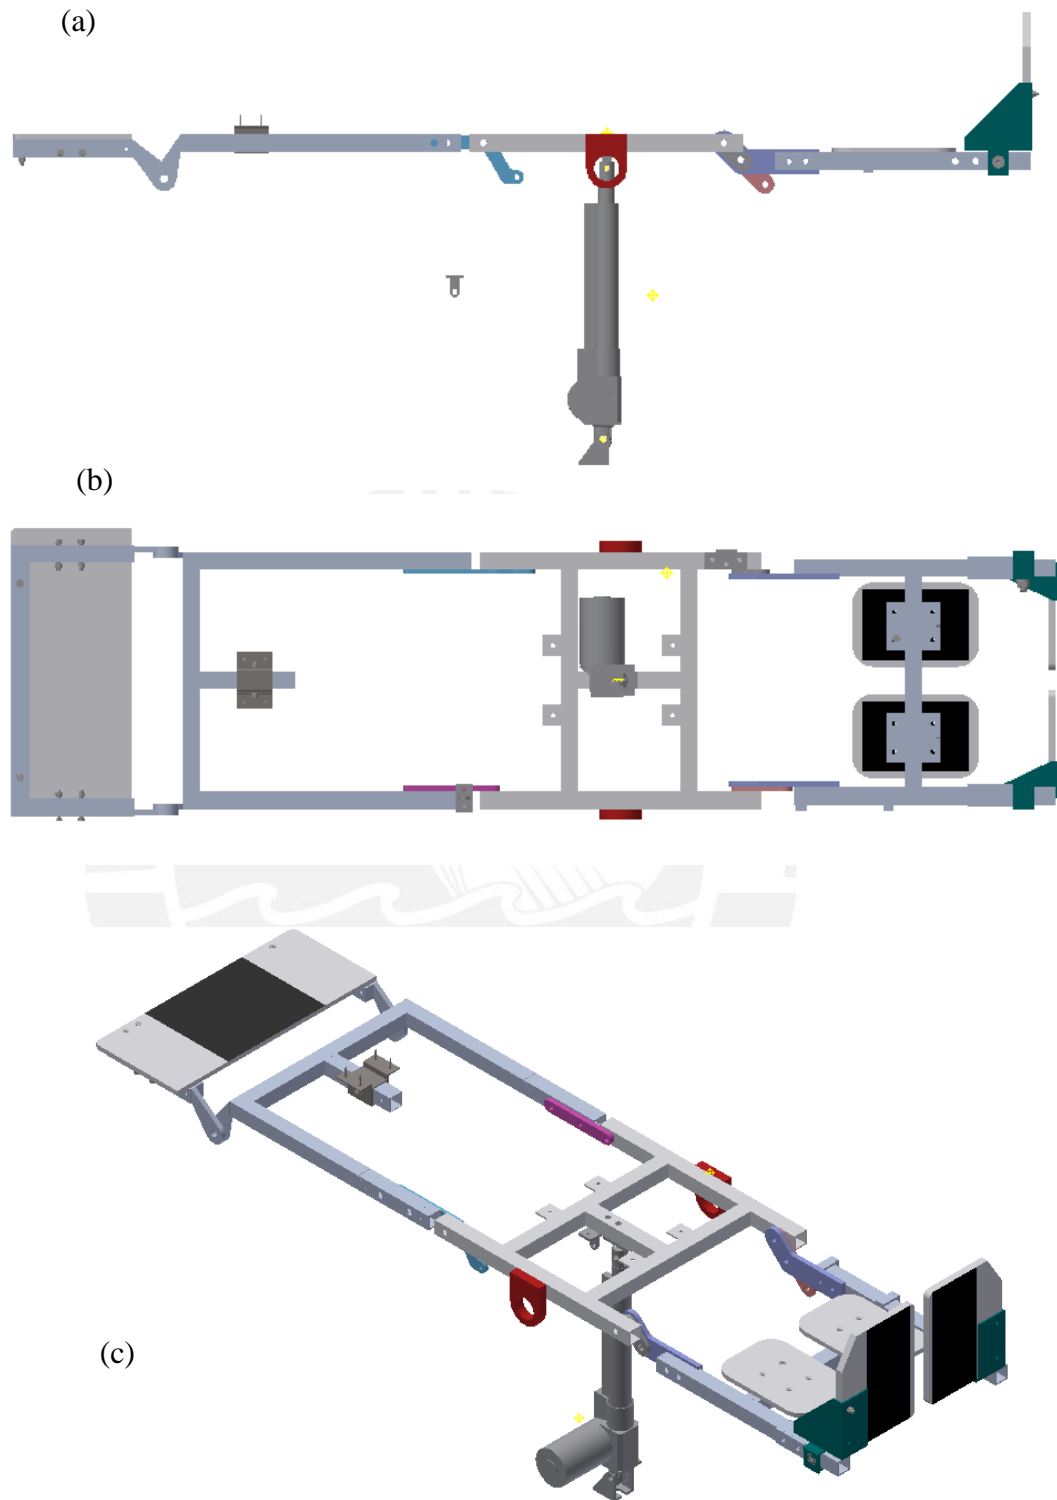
Levantamiento del asiento Vista isométrica, (b) Vista frontal
